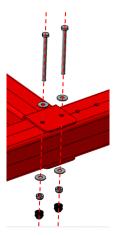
Assemblage de la structure complète (poteaux + traverses longitudinales + traverses latérales) (ZT-L180p)
